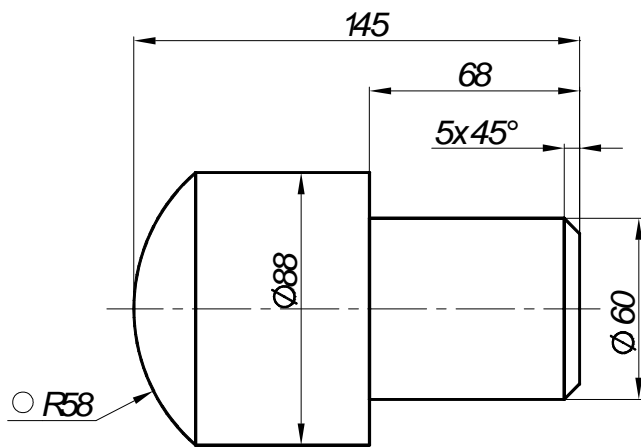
Пример нанесения размеров цилиндров, сферы и конической фаски
